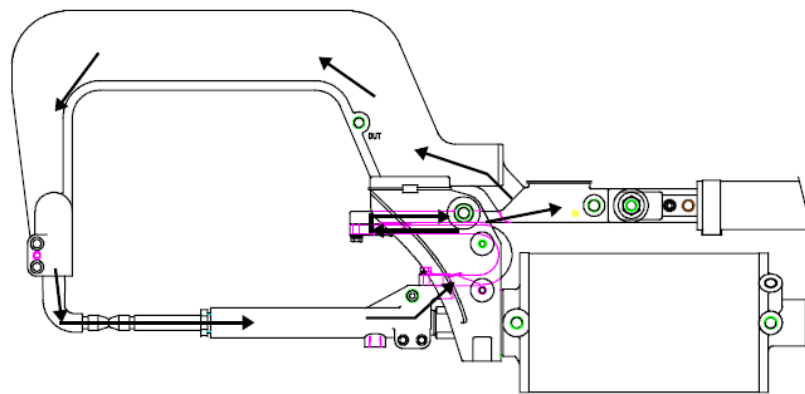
5. Equipo de soldadura por puntos portátil tipo C.
